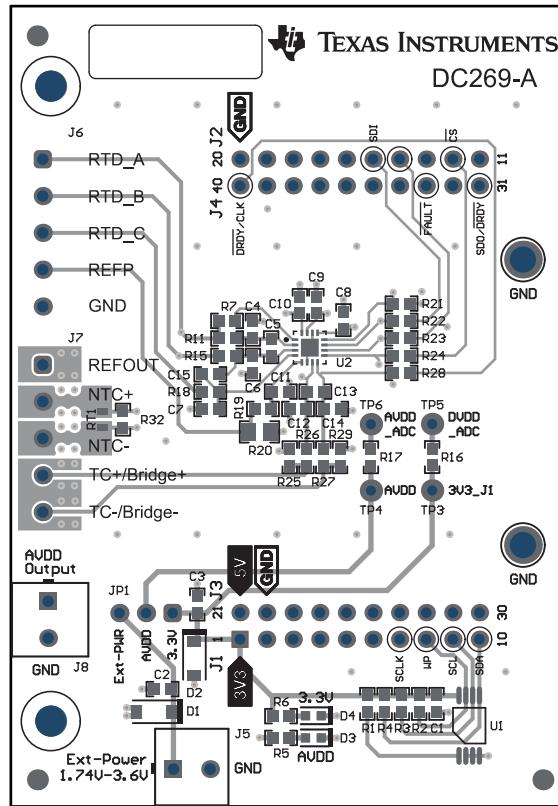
ADS122x14EVM の PCB レイアウト(上面図)
